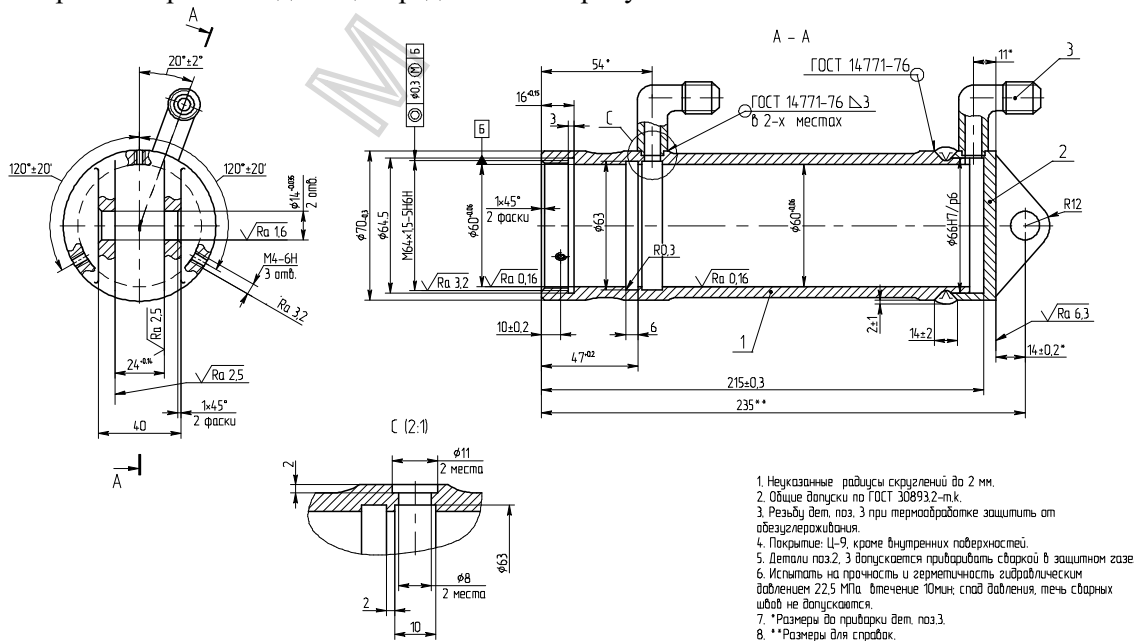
Сборочный чертеж «Цилиндра гидроусилителя руля»
